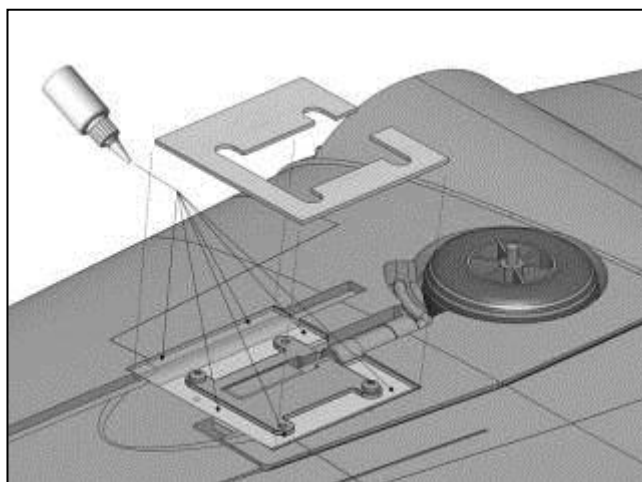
rechtes Fahrwerk in der Tragfläche einlegen und mit 4 Blechschrauben (Pos. 6) verschrauben. Hierzu das Kabel unter dem Sperrholz durchführen und in dem hier vorgesehenen Kabelkanal einlegen.
